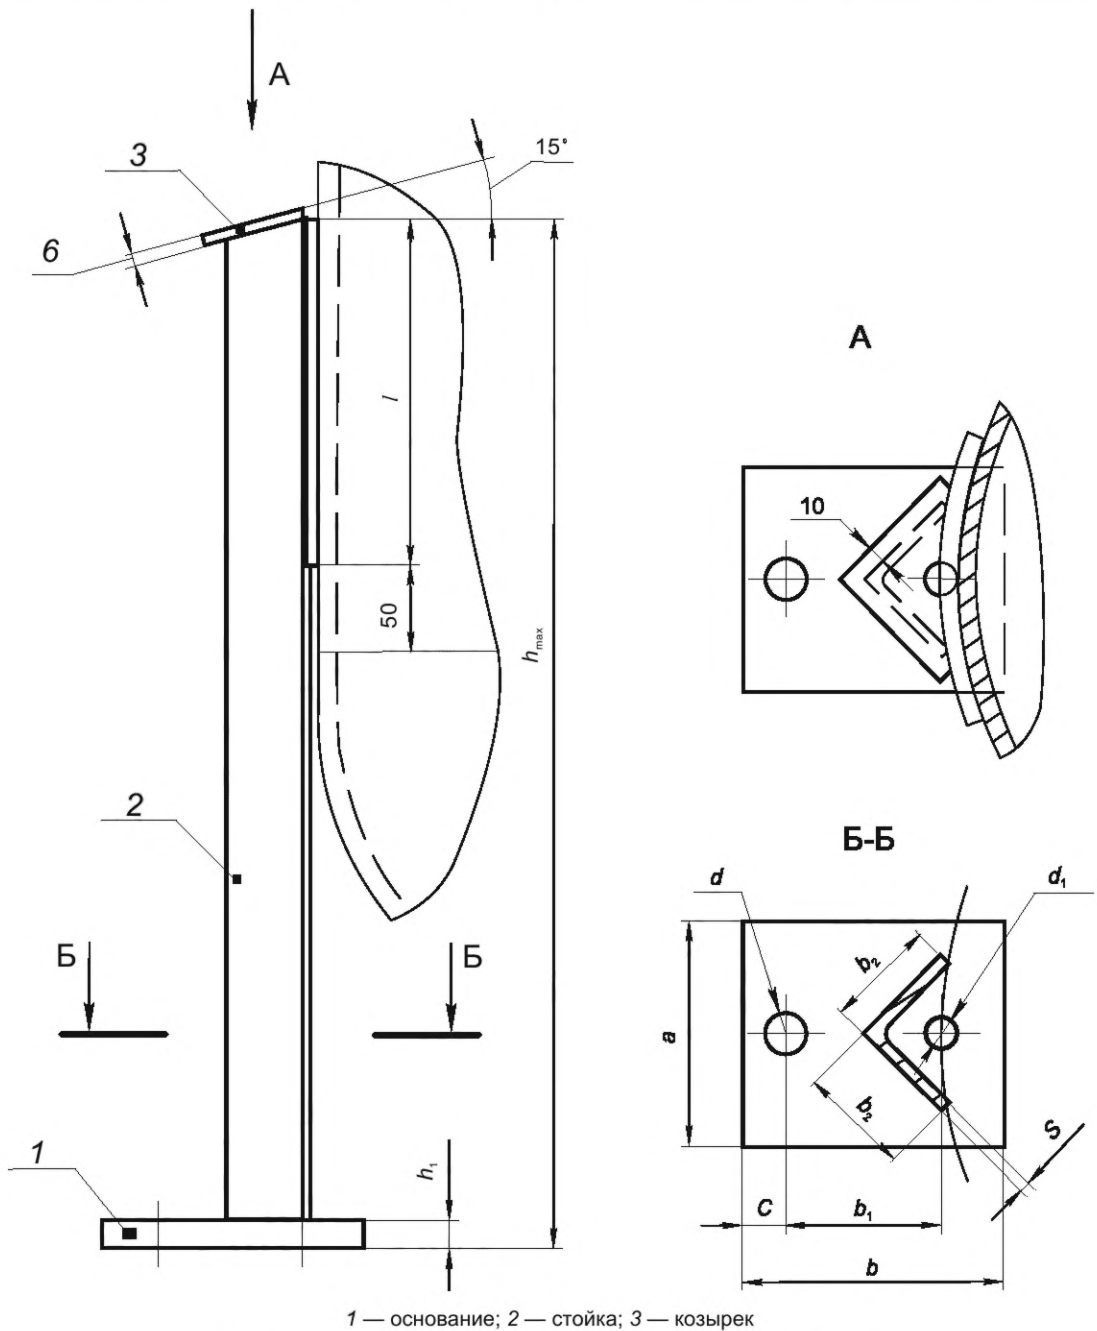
Типовая конструкция опоры вида «С» типа 3
